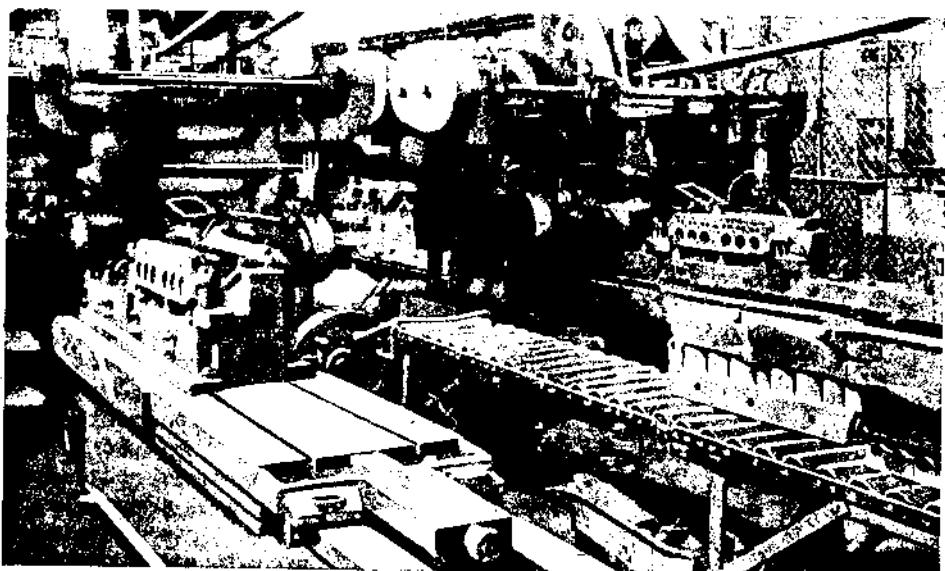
Фрезеровка блоков на продольно-фрезерных станках.
